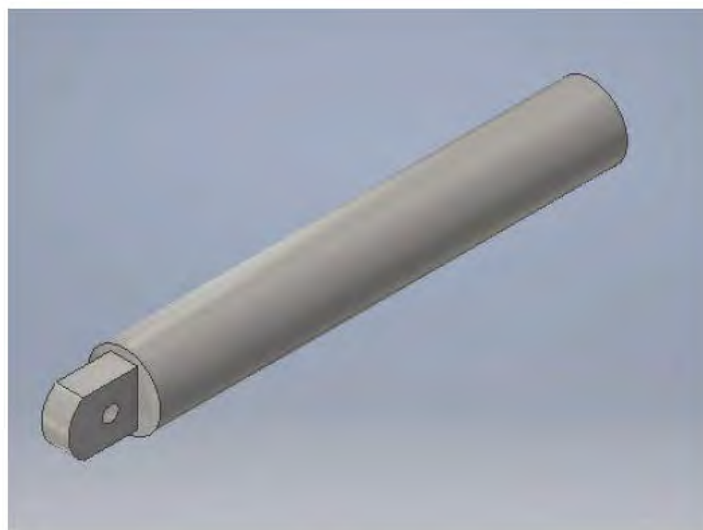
Guía principal de la máquina para aplicar pintura epóxica.
